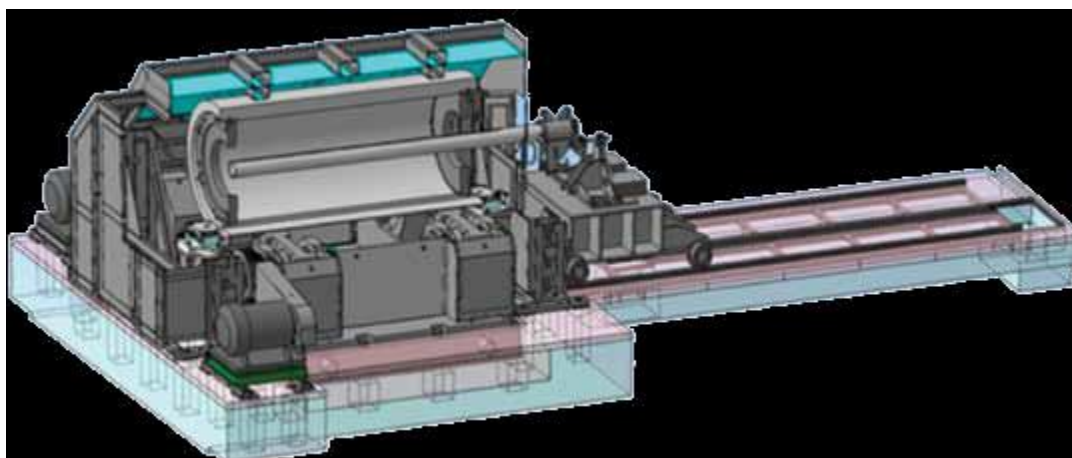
Машина для центробежного литья РМЦ-1000
